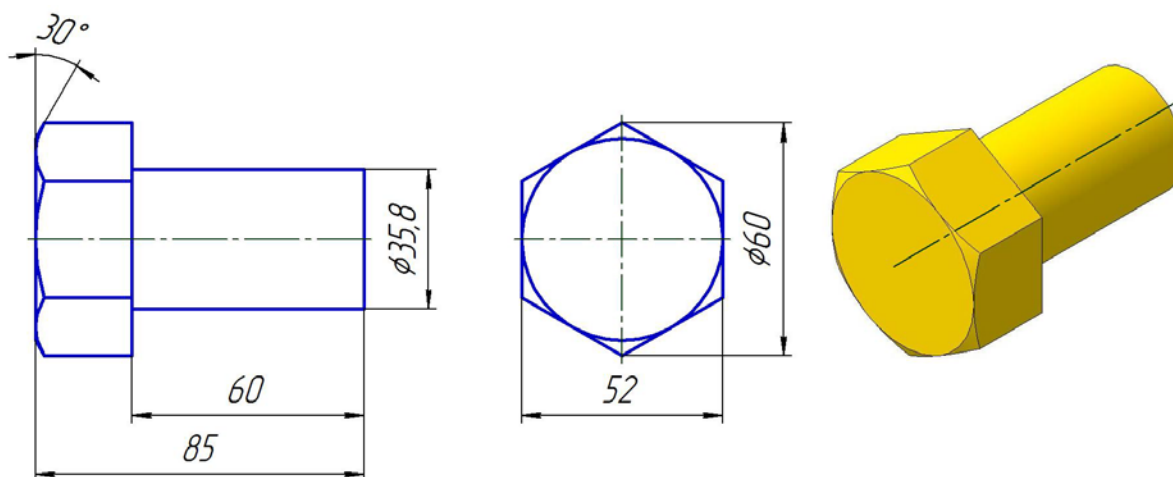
Чертеж и модель заготовки детали «Пробка»
